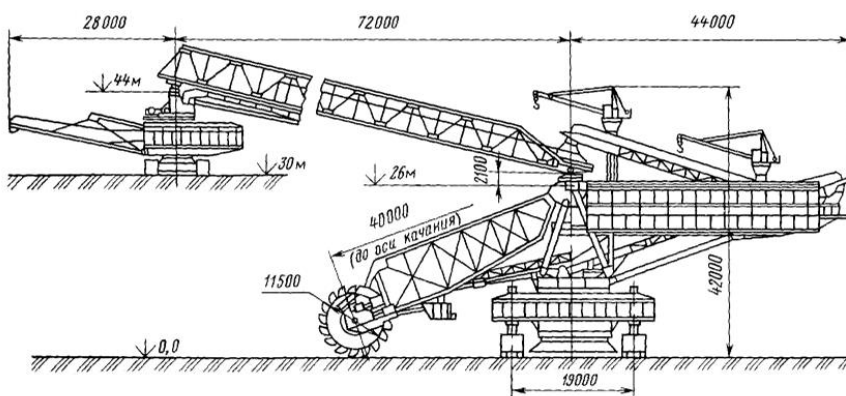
Конструктивная схема роторного экскаватора ЭРП-5250В с верхней погрузкой
